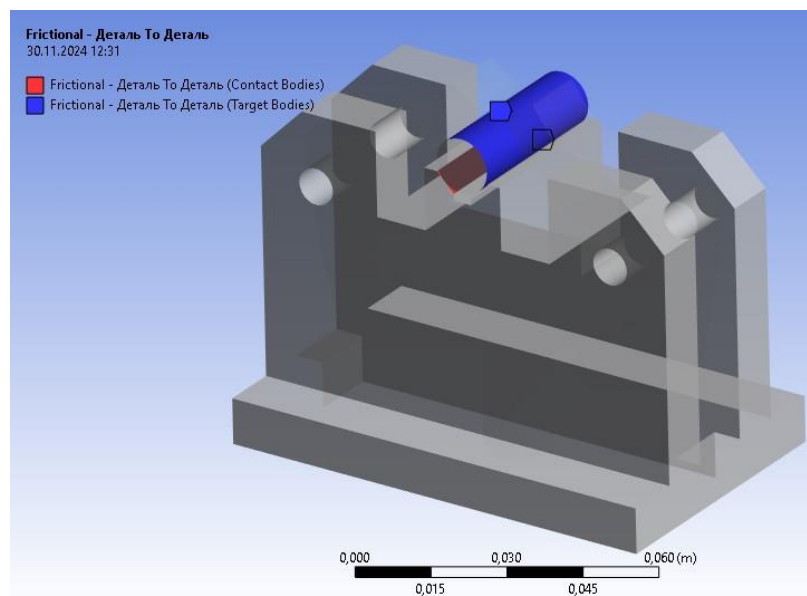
Поверхні контакту циліндричної поверхні зі призмою
